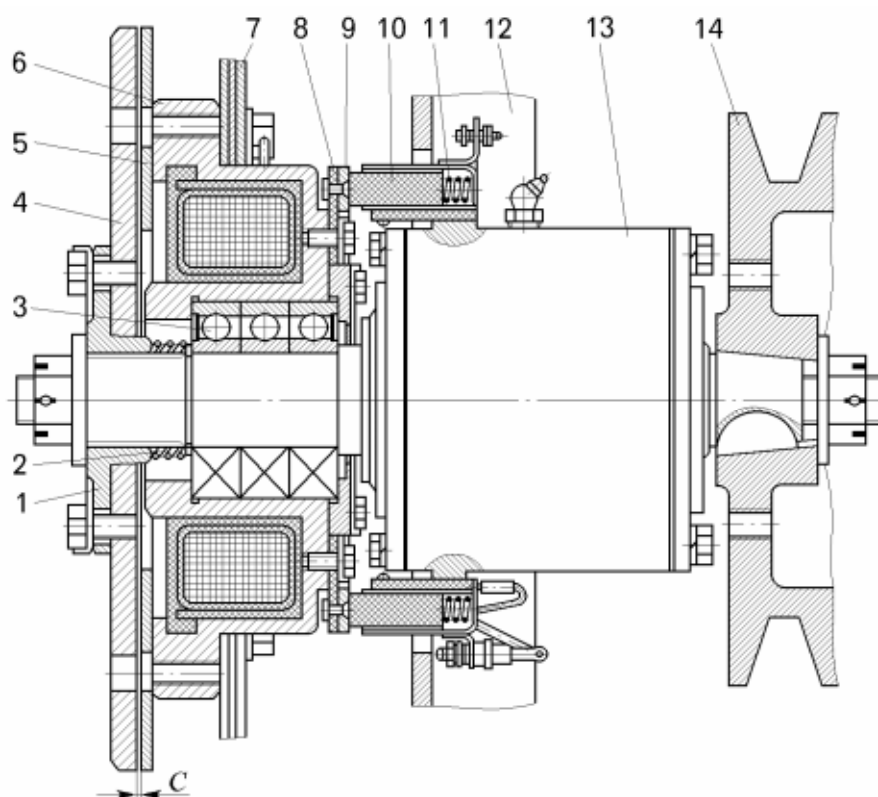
Ведомый шкив привода вентилятора измененной конструкции :
